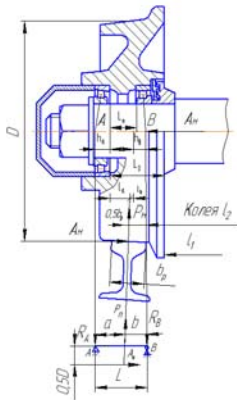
Схема для определения нагрузок на подшипники колеса вагонетки
